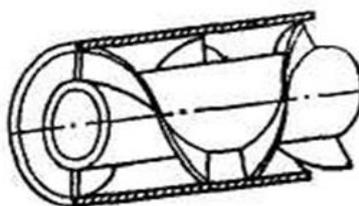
Конструктивное решение, согласно которому винтовые элементы расположены на поверхности центральной трубы либо вала кавитатора
